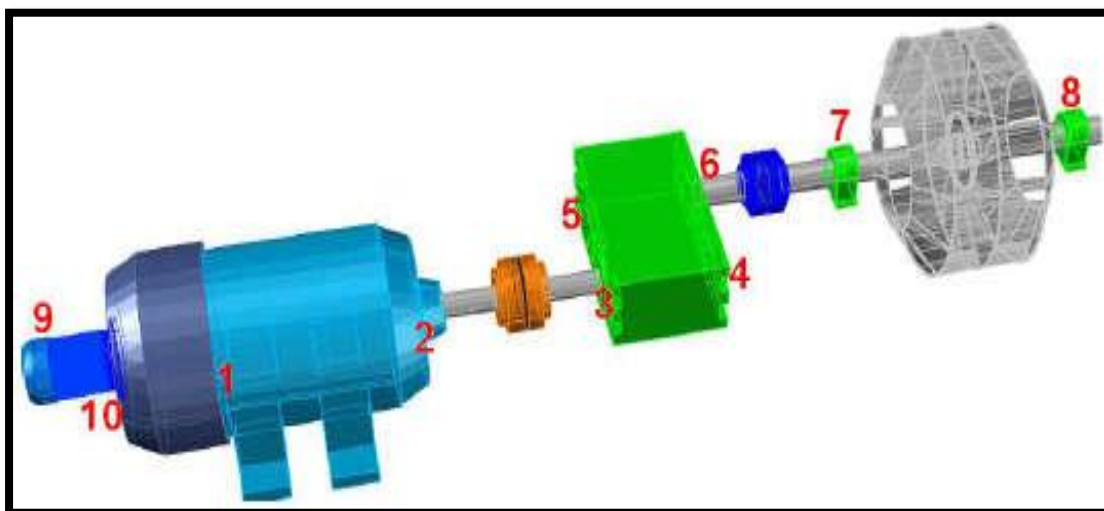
1. Diseño de motor acoplado a un ventilador.
